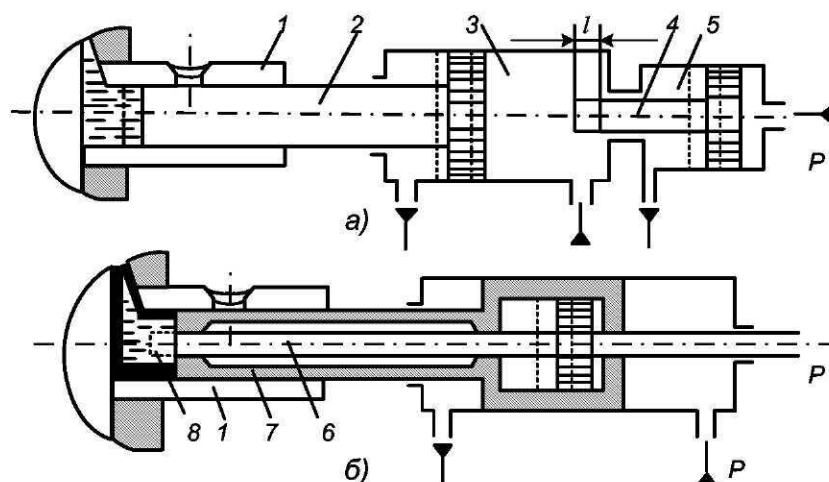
Схема подпрессовки отливок при литье под давлением:
